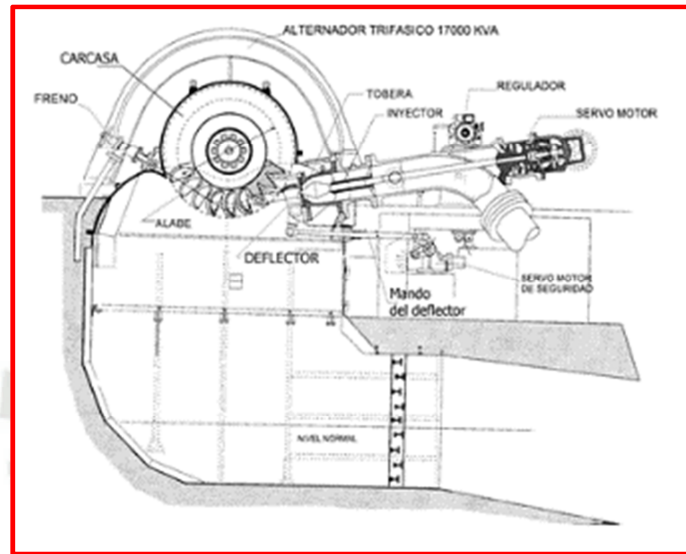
Partes principales de una Turbina Pelton de Eje Horizontal y un inyector.
